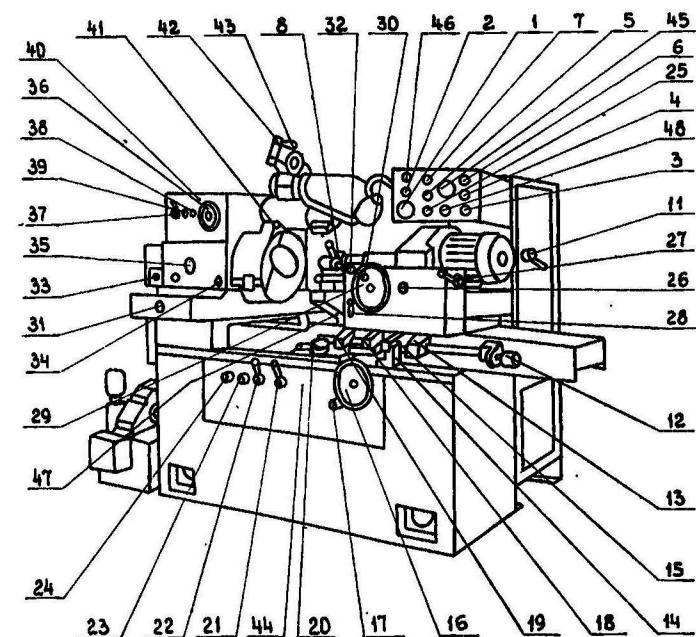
Общий вид станка модели ЗК227А с обозначением органов управления и наялки
